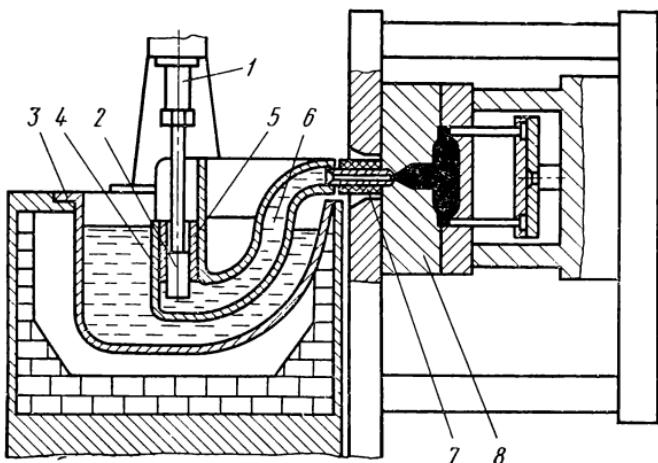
Схема процесса литья под давлением в машине с горячей камерой прессования:
